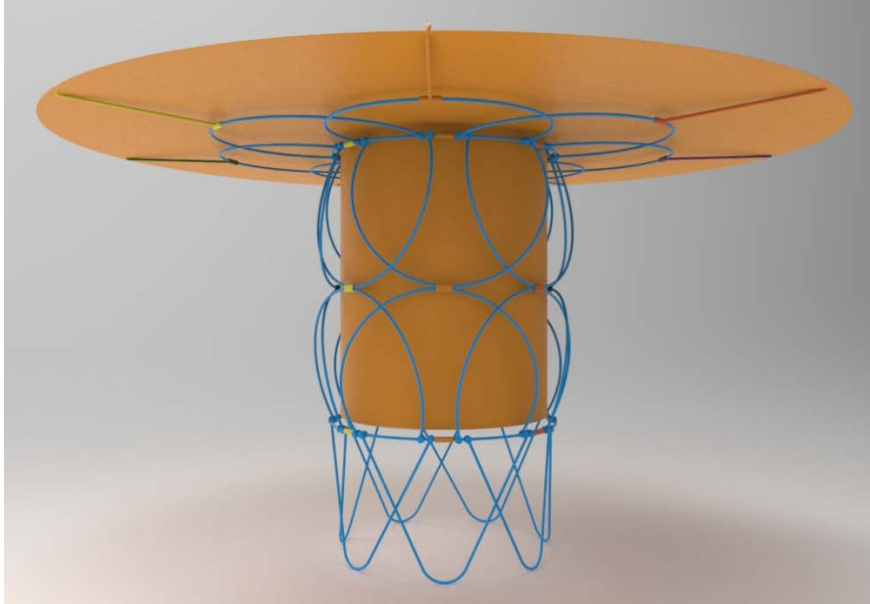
vista del conjunto del refugio solar: estructura y tela.
